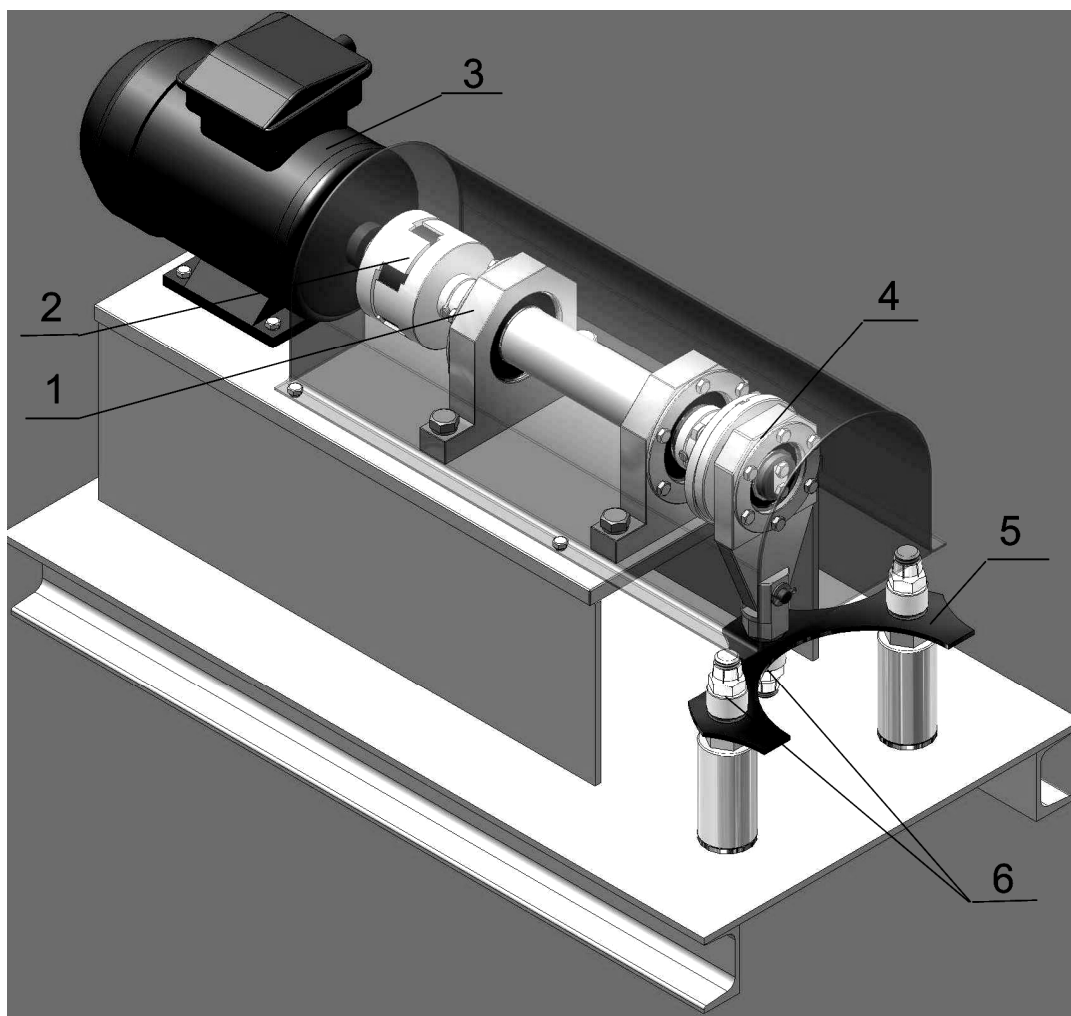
Стенд для випробування на фретинг-корозію пакетних конструкцій дискових муфт
